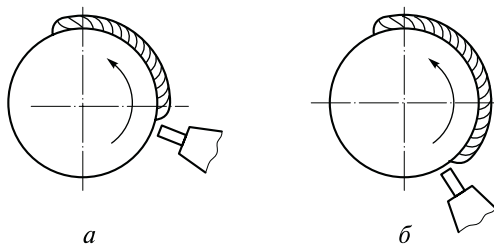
Расположение горелки при сварке кольцевых швов:
